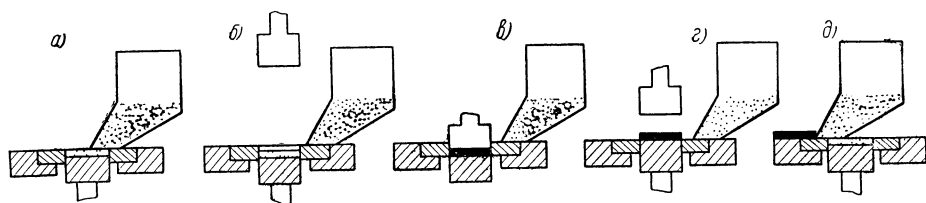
Схема процесса прессования на кулачковом прессе-автомате: а — засыпка пресспорошка в прессформу и снятие избытка массы бункером; б — опускание нижнего пуансона с засыпанным пресспорошком; в — прессование; г — выталкивание заготовки из формы нижним пуансоном; д — сталкивание заготовки бункером и засыпка формы пресспорошком из бункера.
